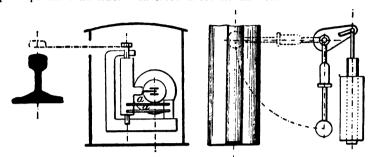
e 5. - Posa-petardi elettrico. Elevazione e pianta.
